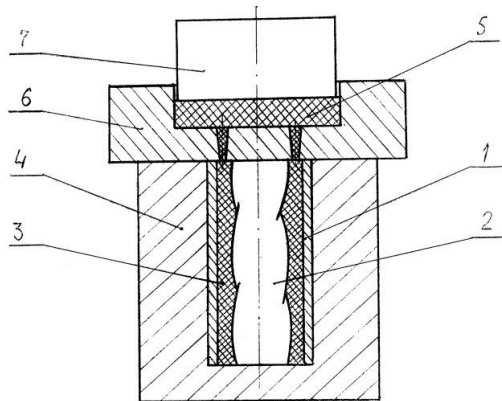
Общий вид формы для прессования: 1 – корпус обоймы; 2 – винтовой стержень с ЦВП; 3 – эластомерный слой; 4 – пресс-форма; 5 – эластомер; 6 – загрузочная камера; 7 – пуансон
